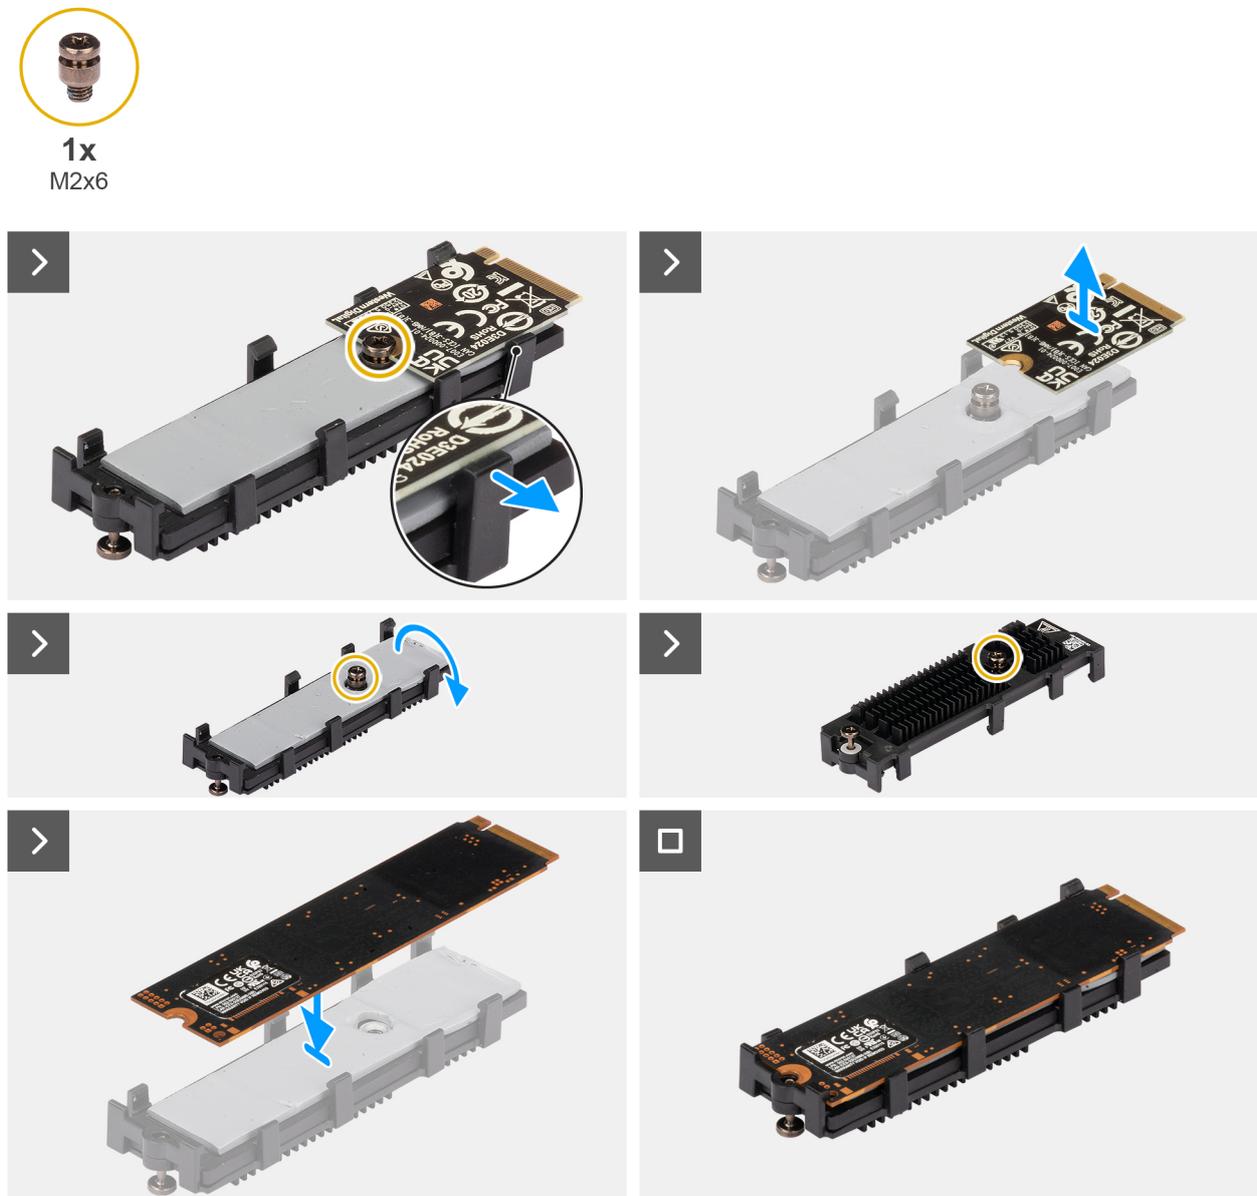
Remplacement du disque SSD M.2 2230 par un disque SSD M.2 2280
